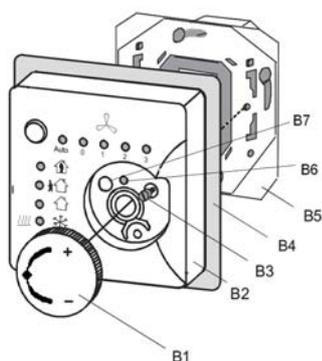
Montage des Fan-Coil Unit Bediengerätes
